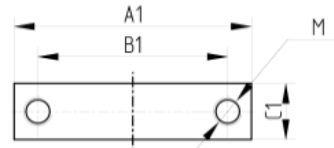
Набор для параллельной установки двигателя и редуктора PM-MKCR
